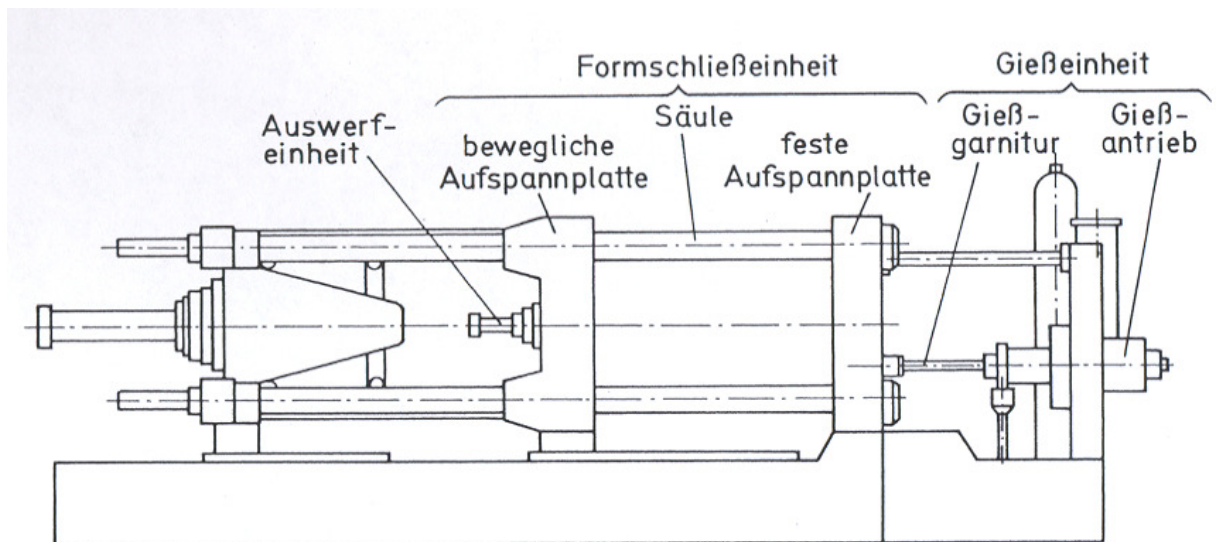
Baugruppen einer Druckgießmaschine nach DIN 24480
